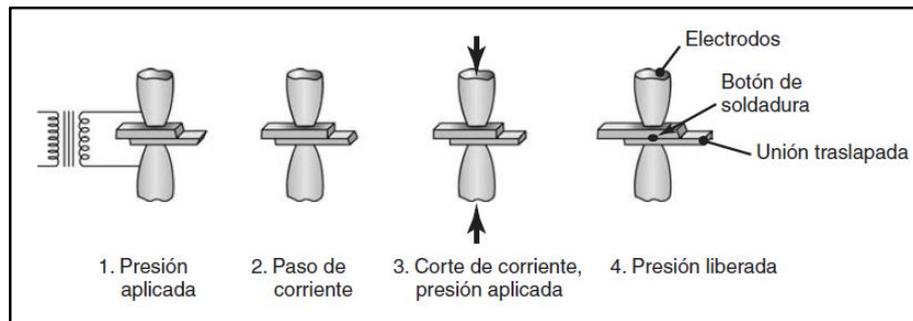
Secuencia de eventos en la soldadura por resistencia por puntos.
